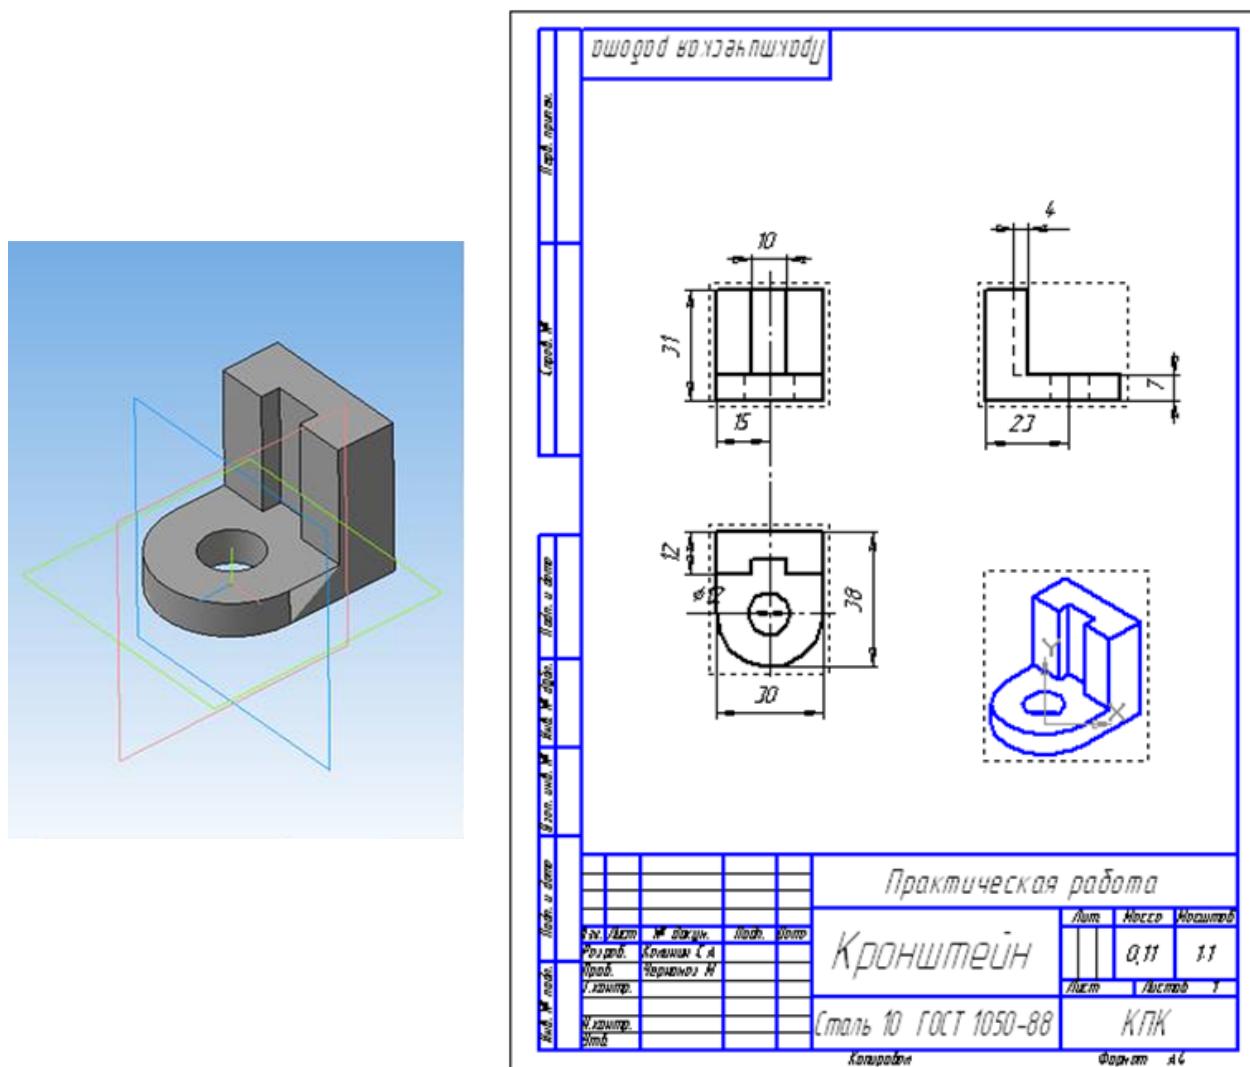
Модель и заготовка чертежа детали Кронштейн.
